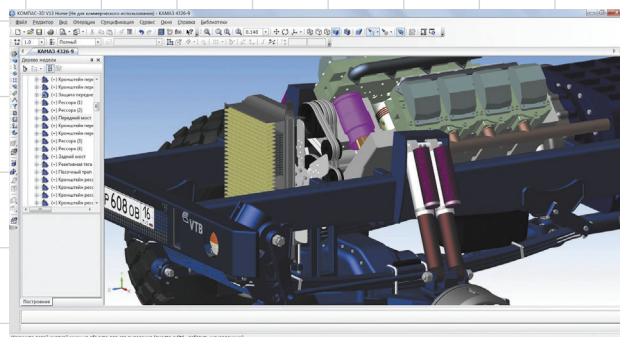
Вид на двигатель, радиатор, амортизаторы и рессоры
